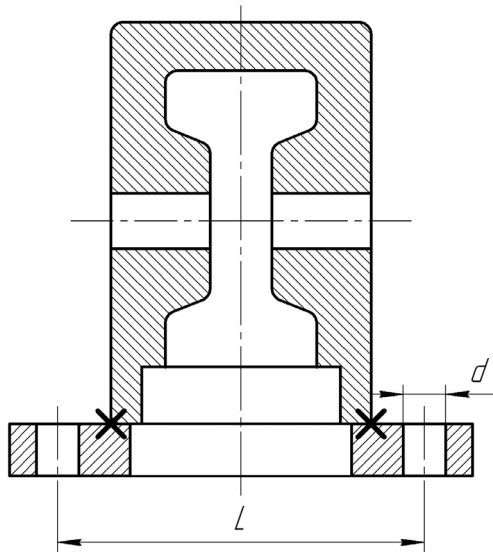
Схема применения искусственной технологической базы для установки корпусной детали
